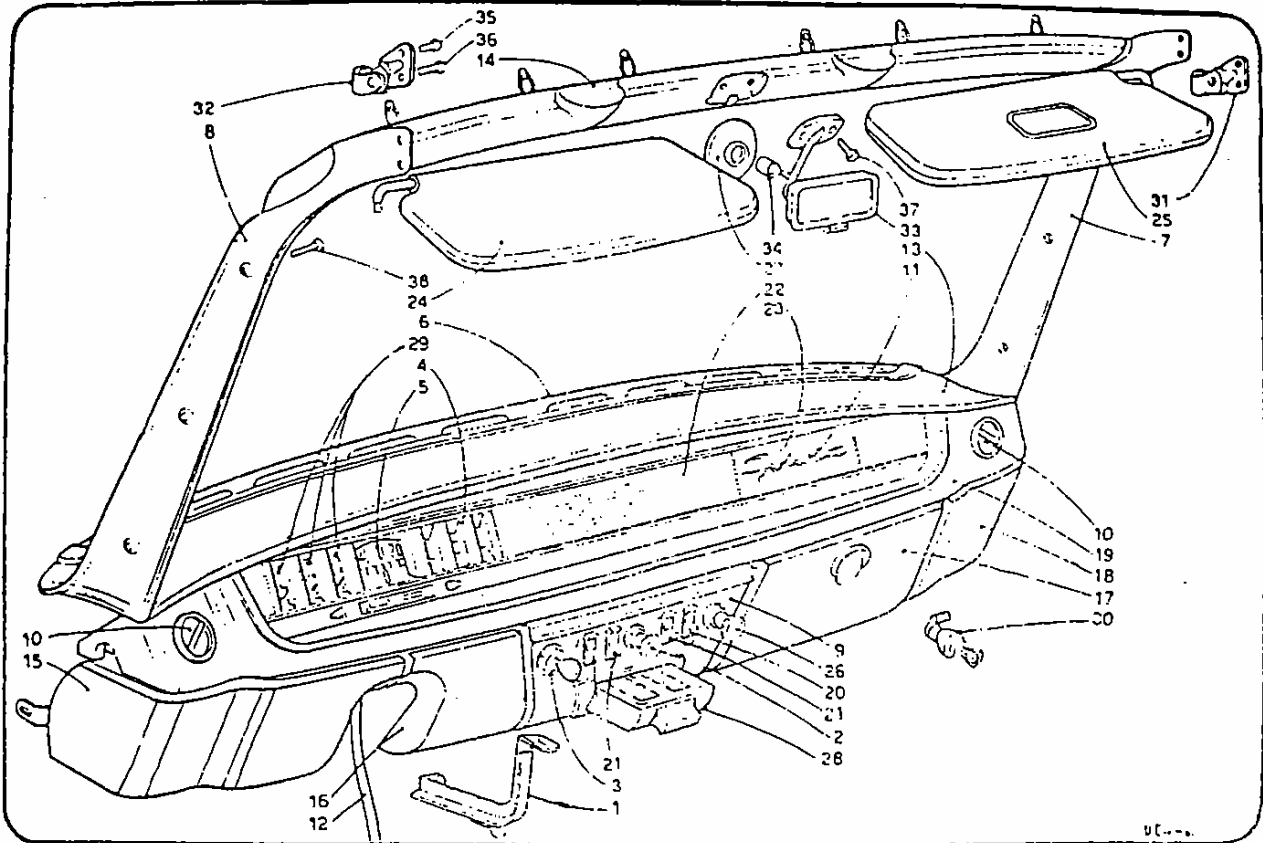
/11 - Equipement planche de bord - Rembourrages (du Catalogue Pièces Détachées).
